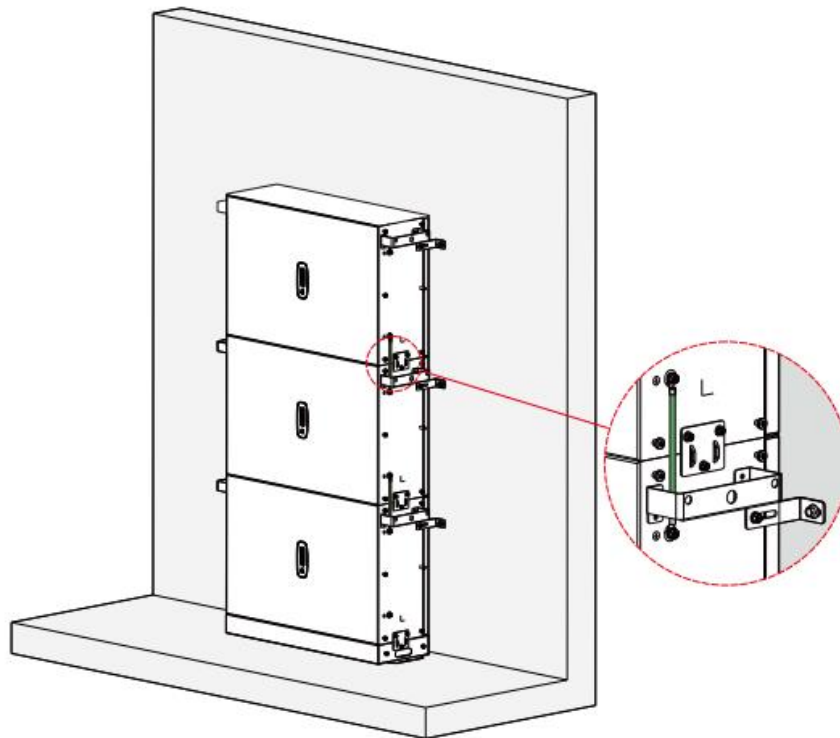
Collegamento del Conduttore di Terra di Protezione Interno
